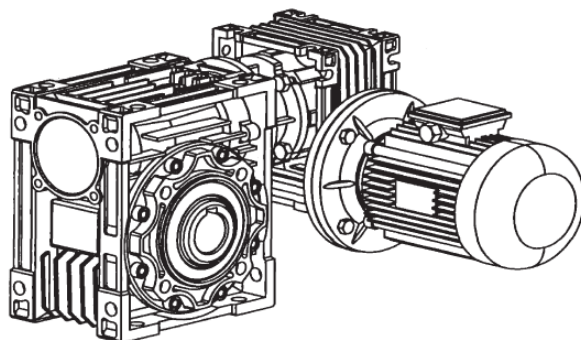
Двухступенчатый червячный мотор-редуктор фирмы *MOTOVARIO
